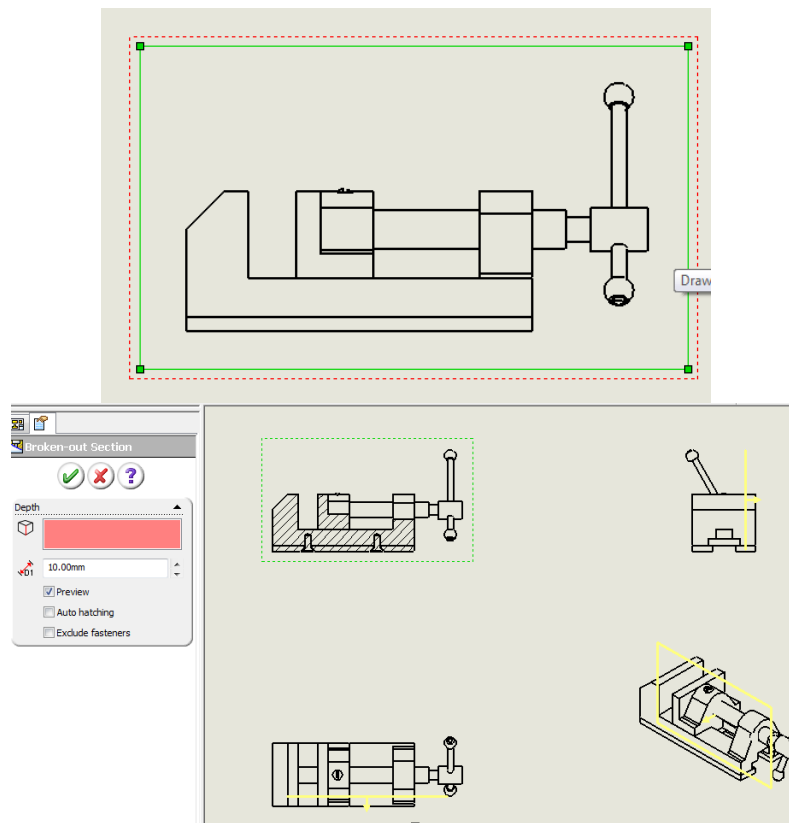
Створення розрізу деталі за допомогою інструменту ВЫРЫВ ДЕТАЛИ (Broken-out Section)
